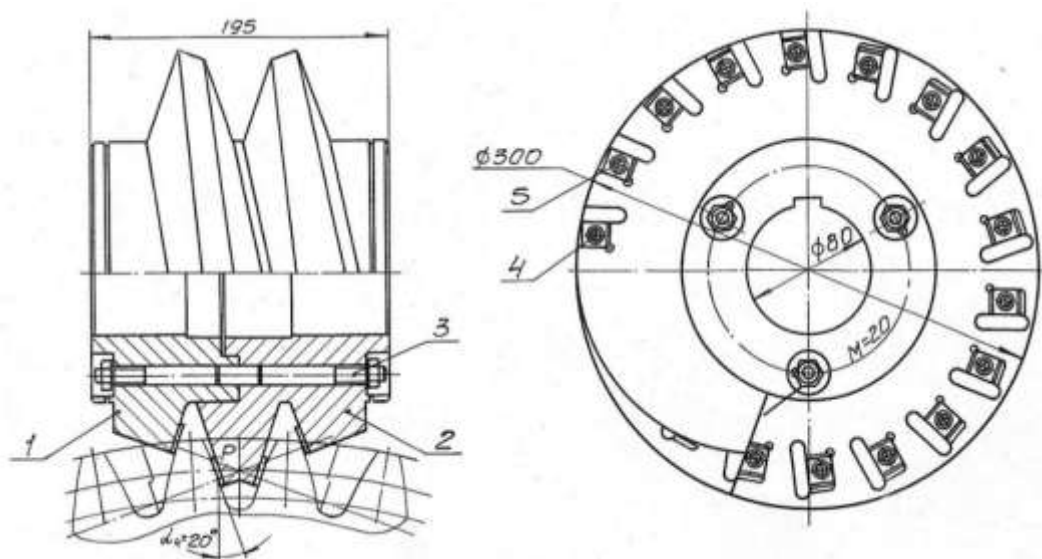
Конструкція збірної фрези двостороннього різання.
